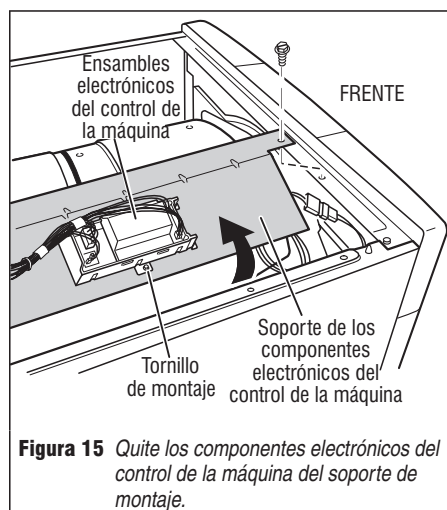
Quite los componentes electrónicos del control de la máquina del soporte de montaje.
